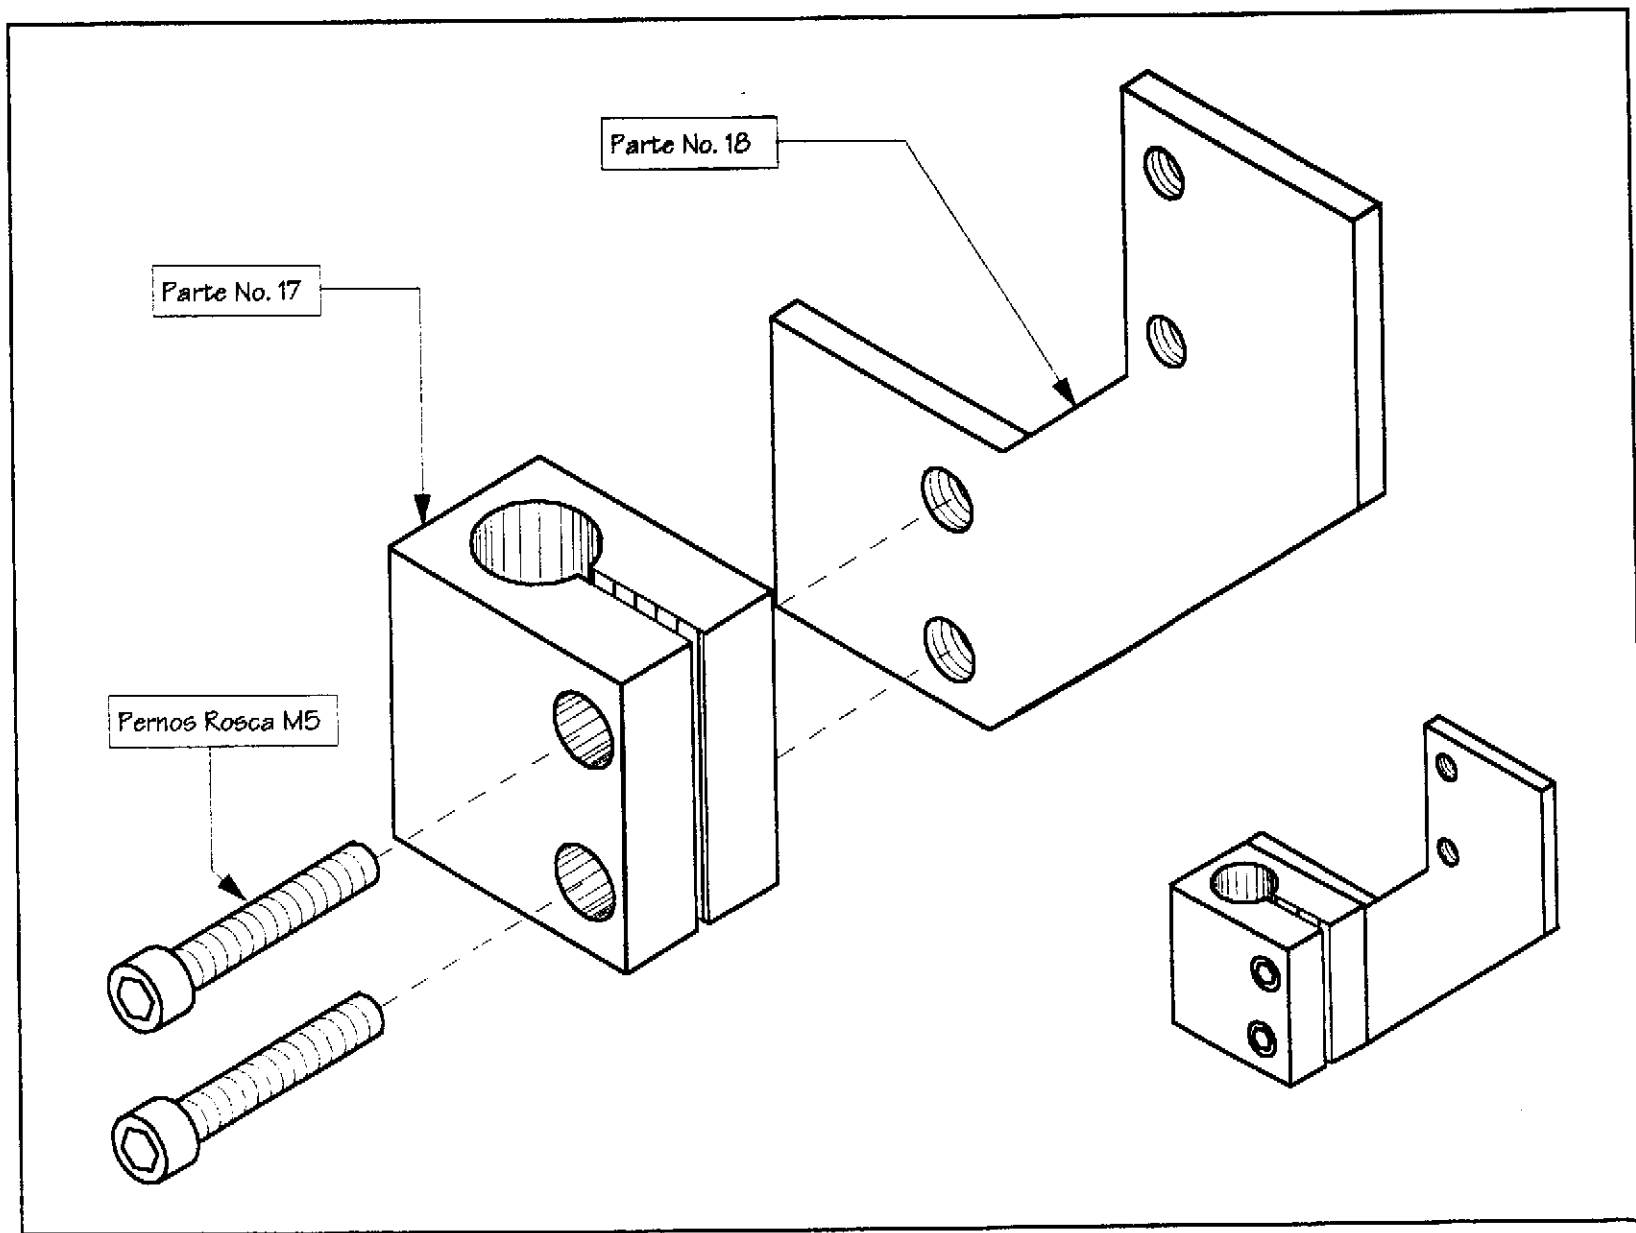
Ensamble del soporte del interruptor de rodillo.
